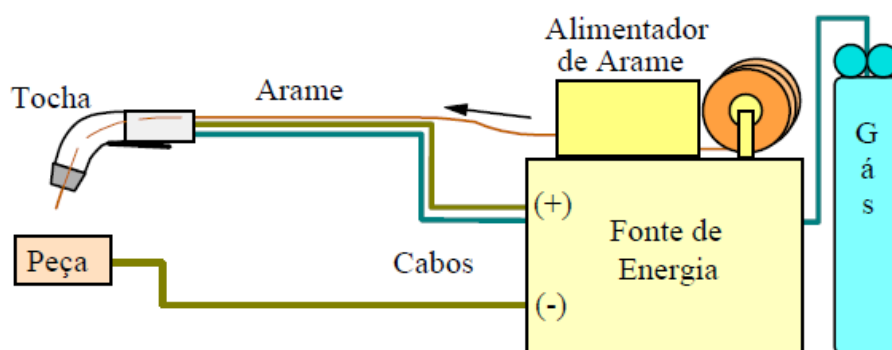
Equipamento para soldagem *FCAW*.
